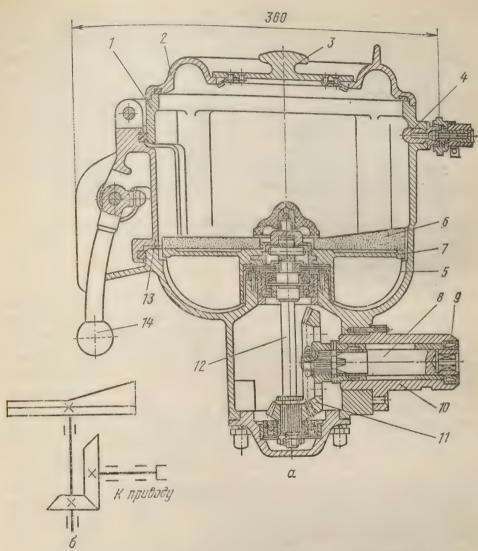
Сменный картофелеочистительный механизм УММ-5: а - общий вид; б - кинематическая схема
